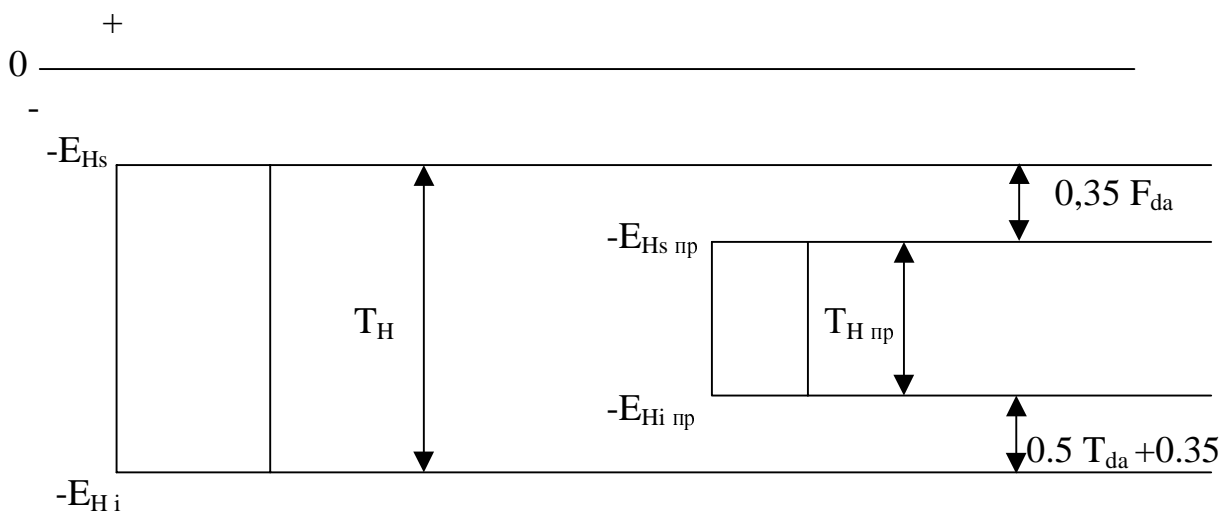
Схема розташування поля допуску на зміщення вихідного контура під час базування приладу на діаметр виступів колеса
